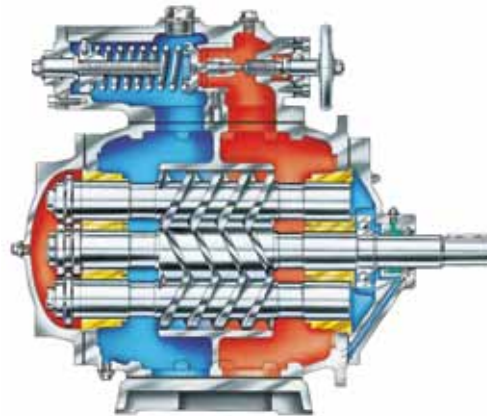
Fünfspindelige Schraubenspindelpumpe
